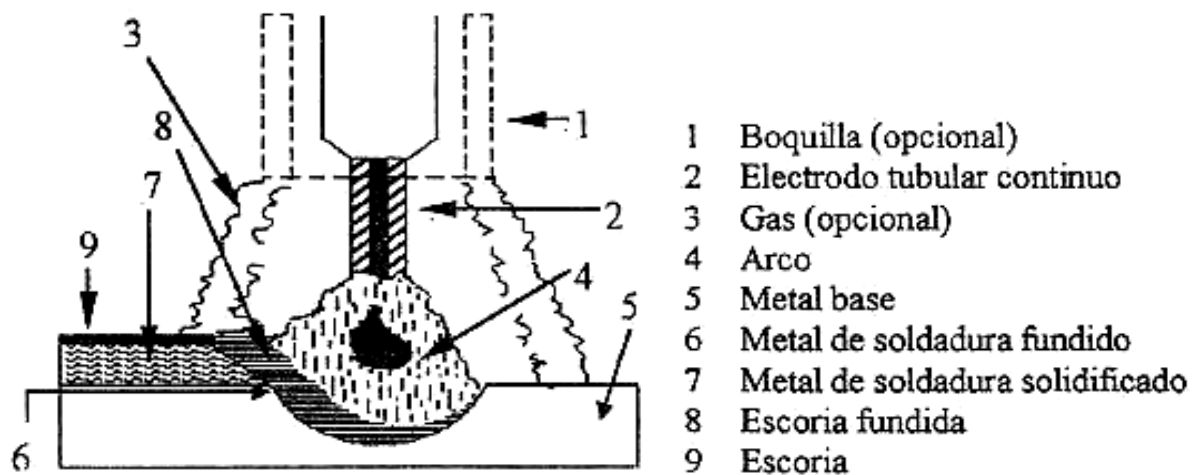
PROCESO DE SOLDADURA POR ARCO CON ELECTRODO TUBULAR CON NÚCLEO DE FUNDENTE.
